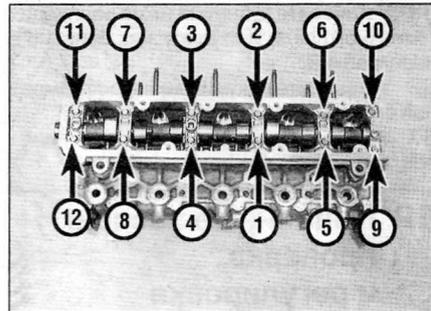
Последовательность затяжки болтов крепления крышек подшипников распределительного вала (двигатели 2.0 л)
